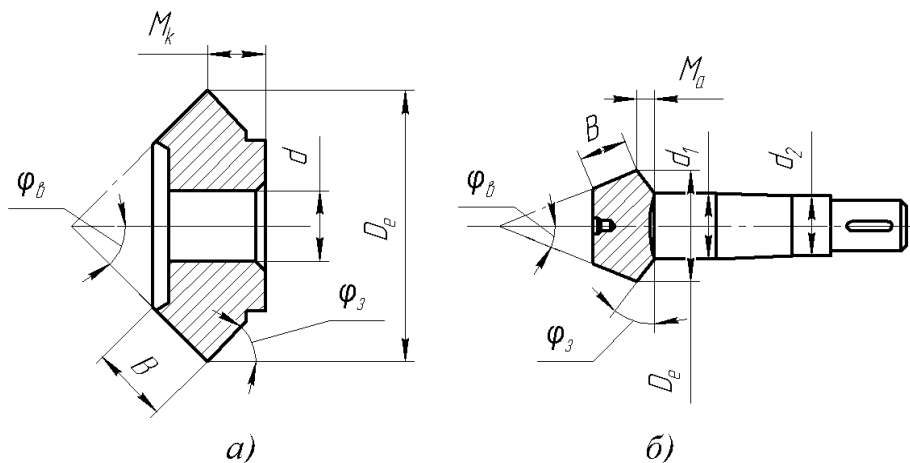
Заготовки конічних зубчастих коліс:
